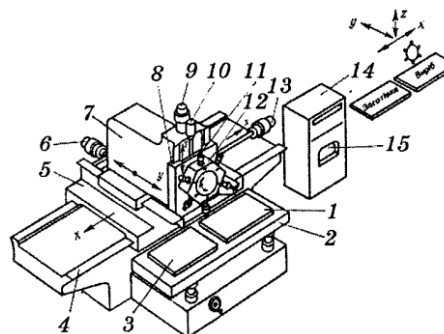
Обробний центр з револьверною головою маятникового типу: 1 – готова деталь; 2 – стіл; 3 – заготовка; 4, 5 – напрямні; 6, 9, 10, 13 – приводні механізми; 7 – колонка; 8 – плита; 11 – різальний інструмент; 12 – револьверна головка; 14 – пульт керування; 15 – мікропроцесор
